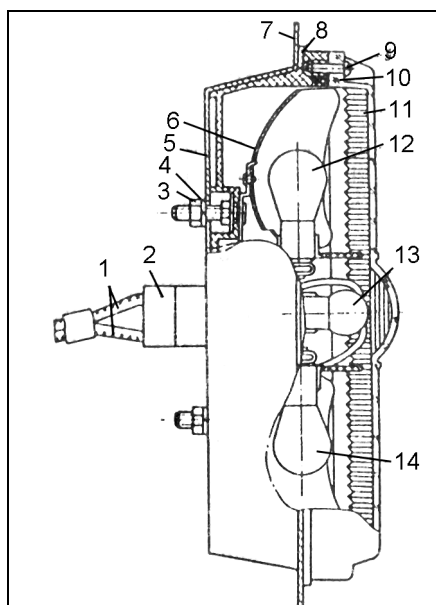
Фонарь задний: 1 – провода основного пучка проводов; 2 – колодка соединительная; 3 – гайка крепления фонаря; 4 – шайба пружинная; 5 – корпус; 6 – узел амортизации в сборе; 7 – кузов; 8 – прокладка; 9 – винт; 10 – прокладка рассеивателя; 11 – рассеиватель; 12 – лампа указателя поворота; 13 – лампа освещения габарита автомобиля; 14 – лампа стоп-сигнала.
